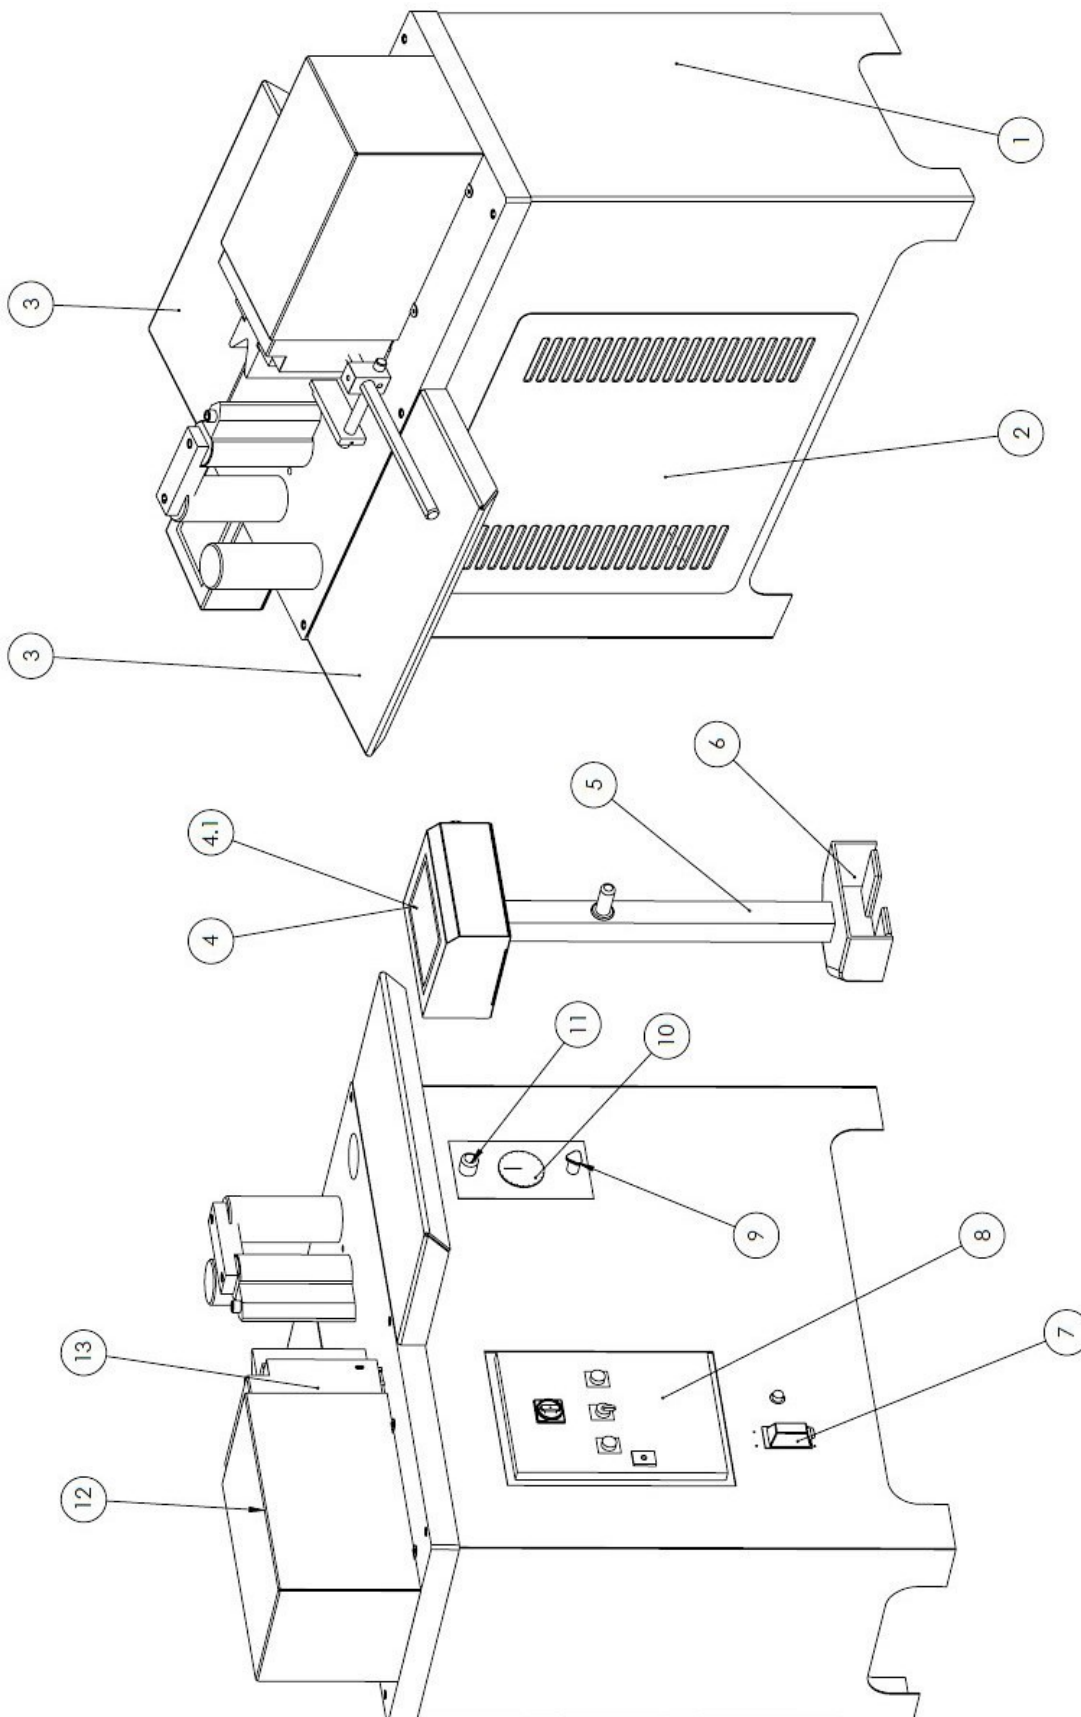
Schéma des pièces 1 Machine complète HBP
